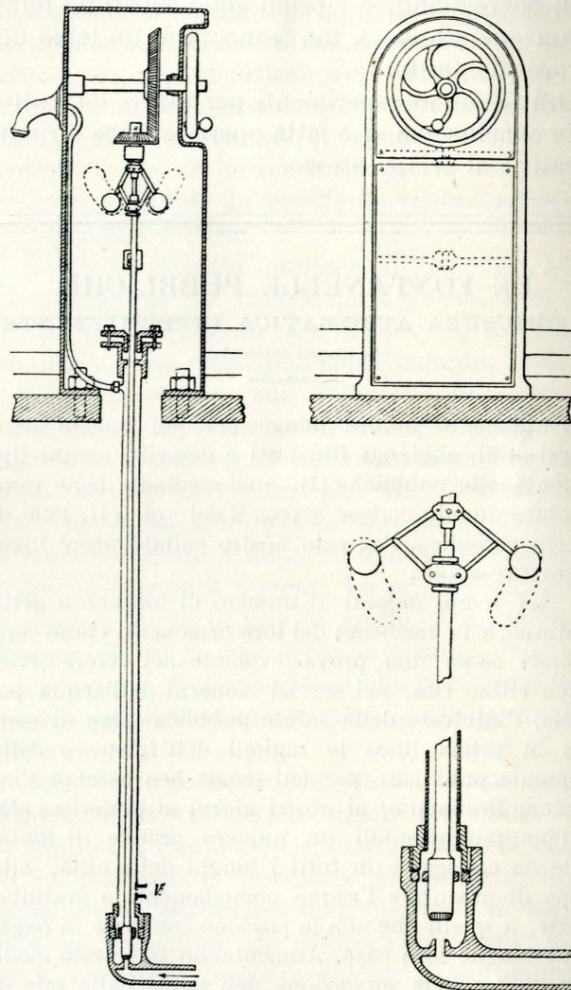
Sezione verticale, prospetto e particolari della fontanella intermittente sistema Bayard.
